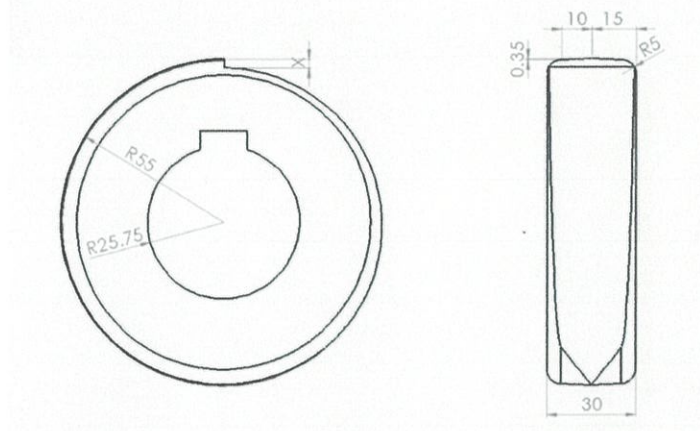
แบบ Drawing และ Dimension ต่างๆของแผ่นล้อ
